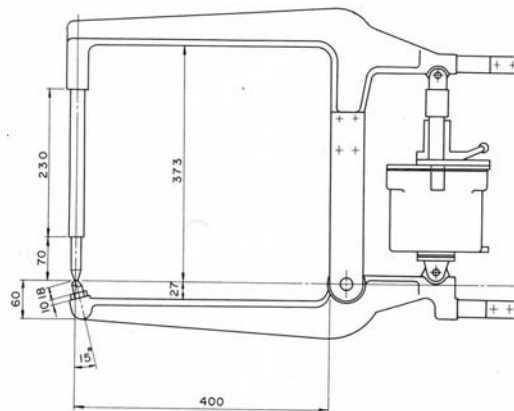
Pistola de soldadura tipo X (AX-204013) ^[11].
